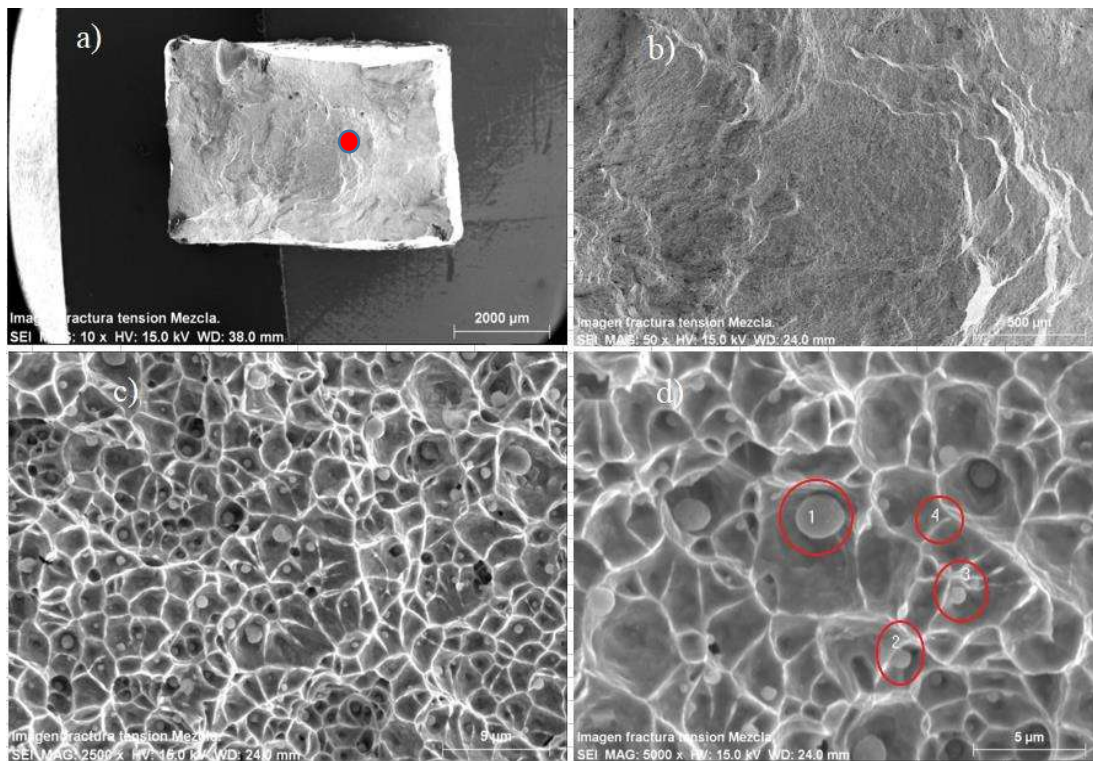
Imágenes de la zona de fractura de la probeta de tensión soldada con mezcla.
